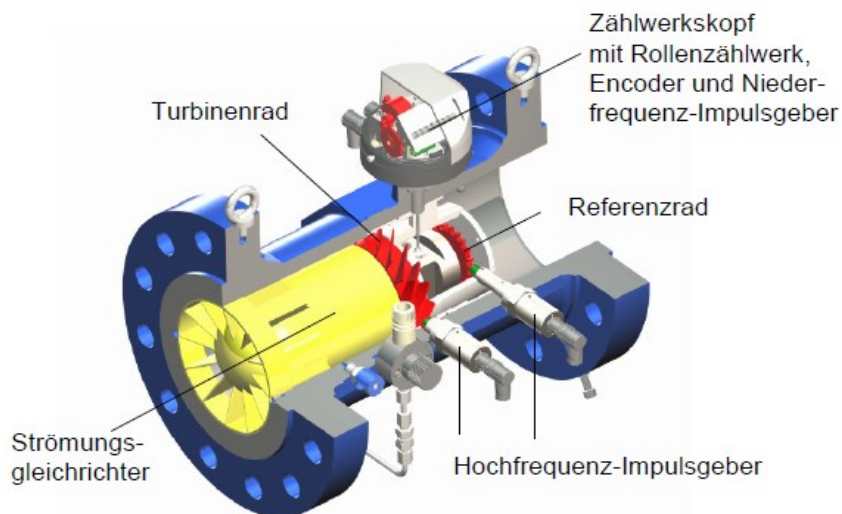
Schnittzeichnung RMG Turbinenradgaszähler
